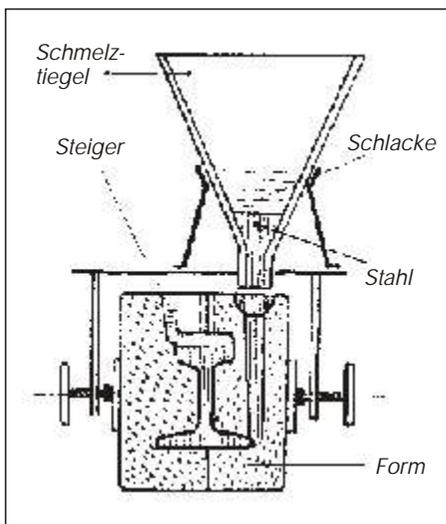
Schema Aluminothermische Schienenschweißung
